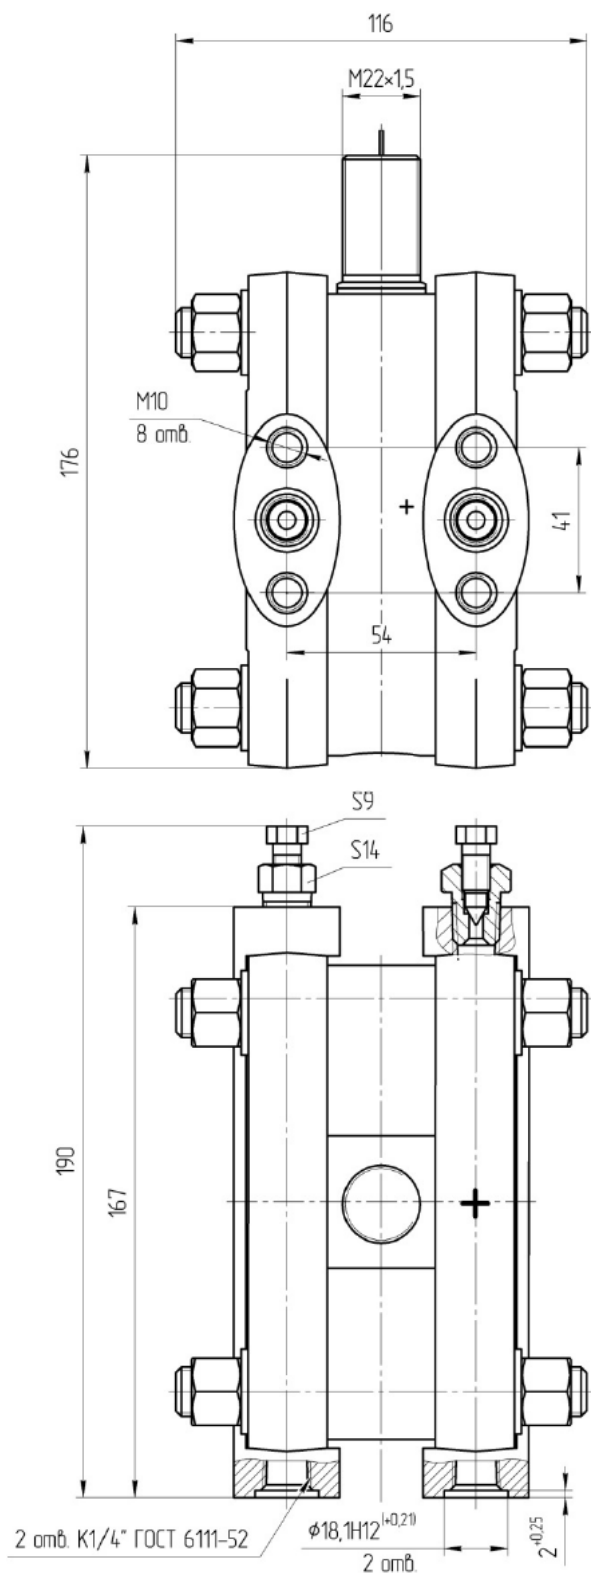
Габаритные и присоединительные размеры преобразователя разности давлений.
